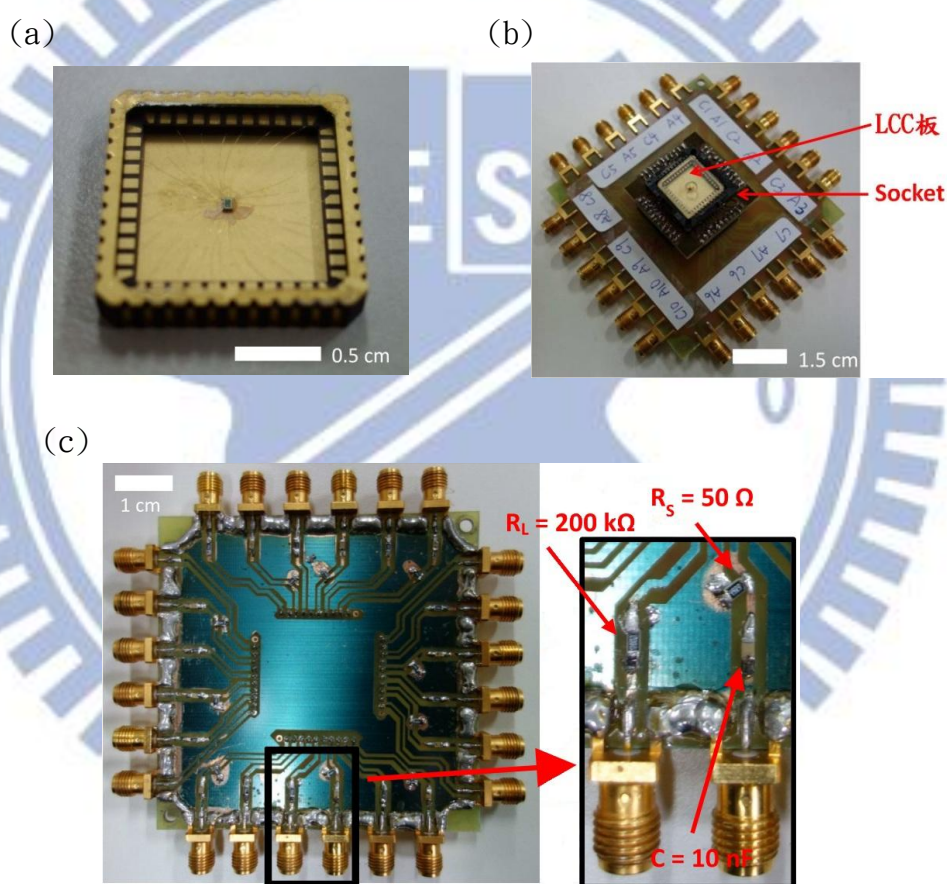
、(a)晶片於 LCC 板上的打線圖 (b)LCC 板透過 socket 轉接到 PCB 板上
